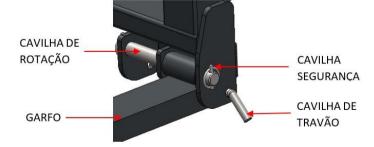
Alteração da posição dos garfos do Elevador.
